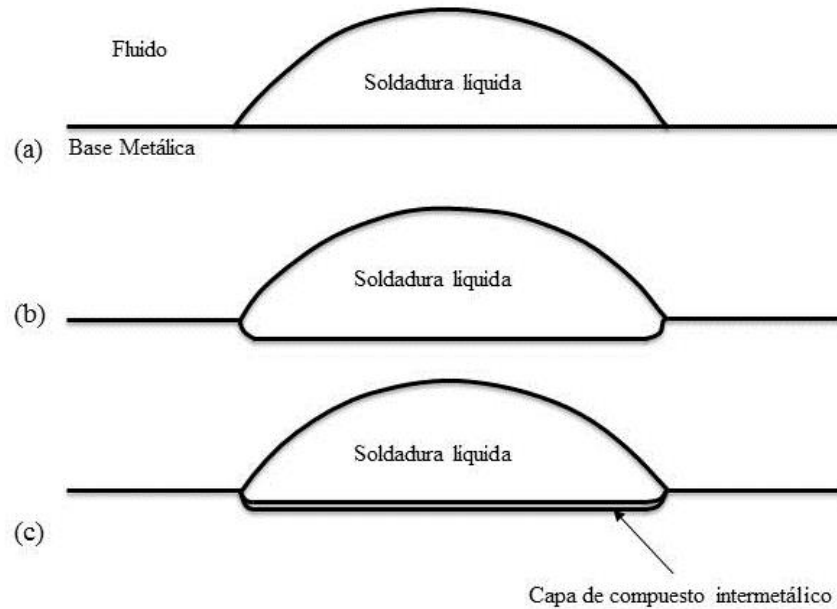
Proceso de soldado (a) soldadura líquida esparcida sobre una base metal, (b) metal-base disuelta en soldadura líquida, (c) Reacción del metal-base con soldadura líquida para formar la capa de compuestos intermetálicos [2].
